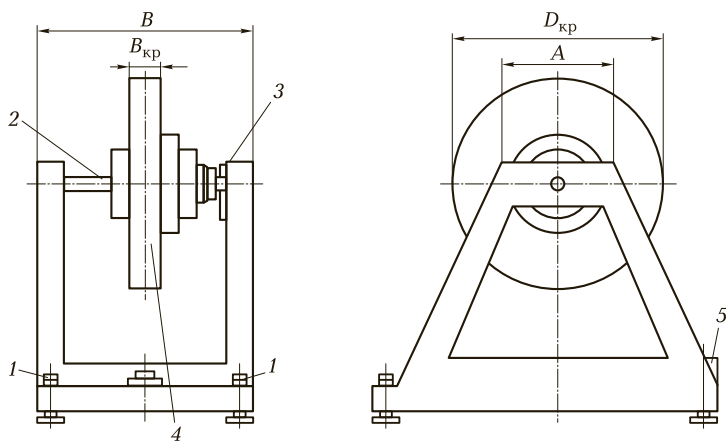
Стенд для балансировки абразивного инструмента:
